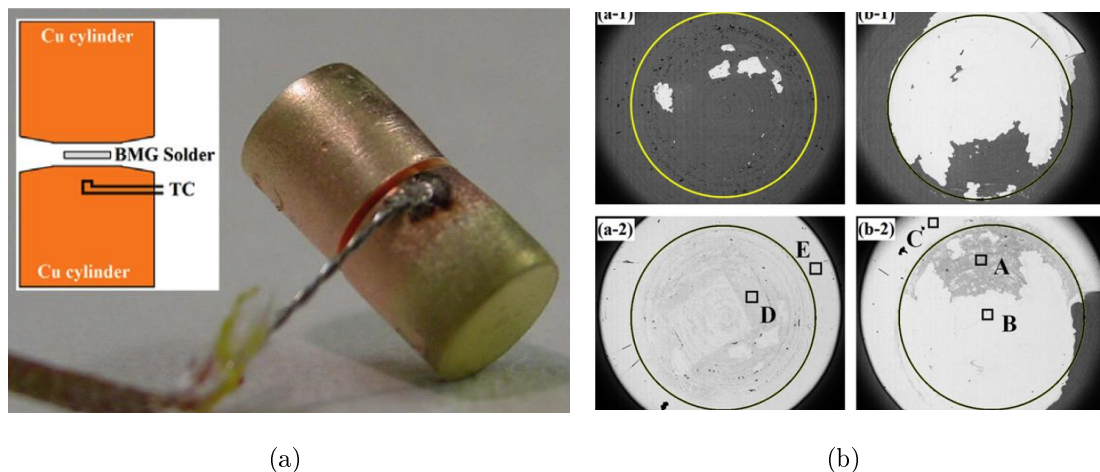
Schéma de la configuration de l'échantillon avant soudage et photo de l'échantillon après soudage (a). Surfaces de rupture d'échantillons soudés à 563 K (a-1 et a-2) et 573 K (b-1 et b-2). Le cuivre apparaît en noir et le verre base-Platine en blanc. Les cercles d'un diamètre de 3 mm représentent la surface initiale du verre métallique (b). [Suh et al., 2008]
